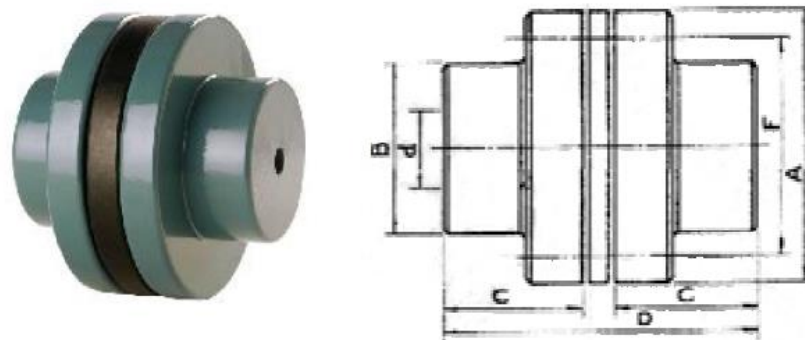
Figura y dimensiones del acoplamiento seleccionado (Fuente: ROTULAR [4]).
